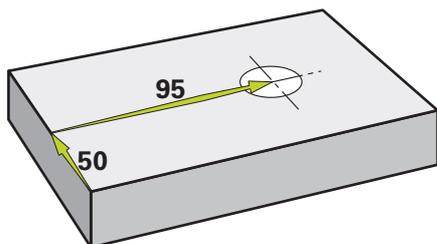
Образцовая деталь – Изготовление сквозного отверстия
